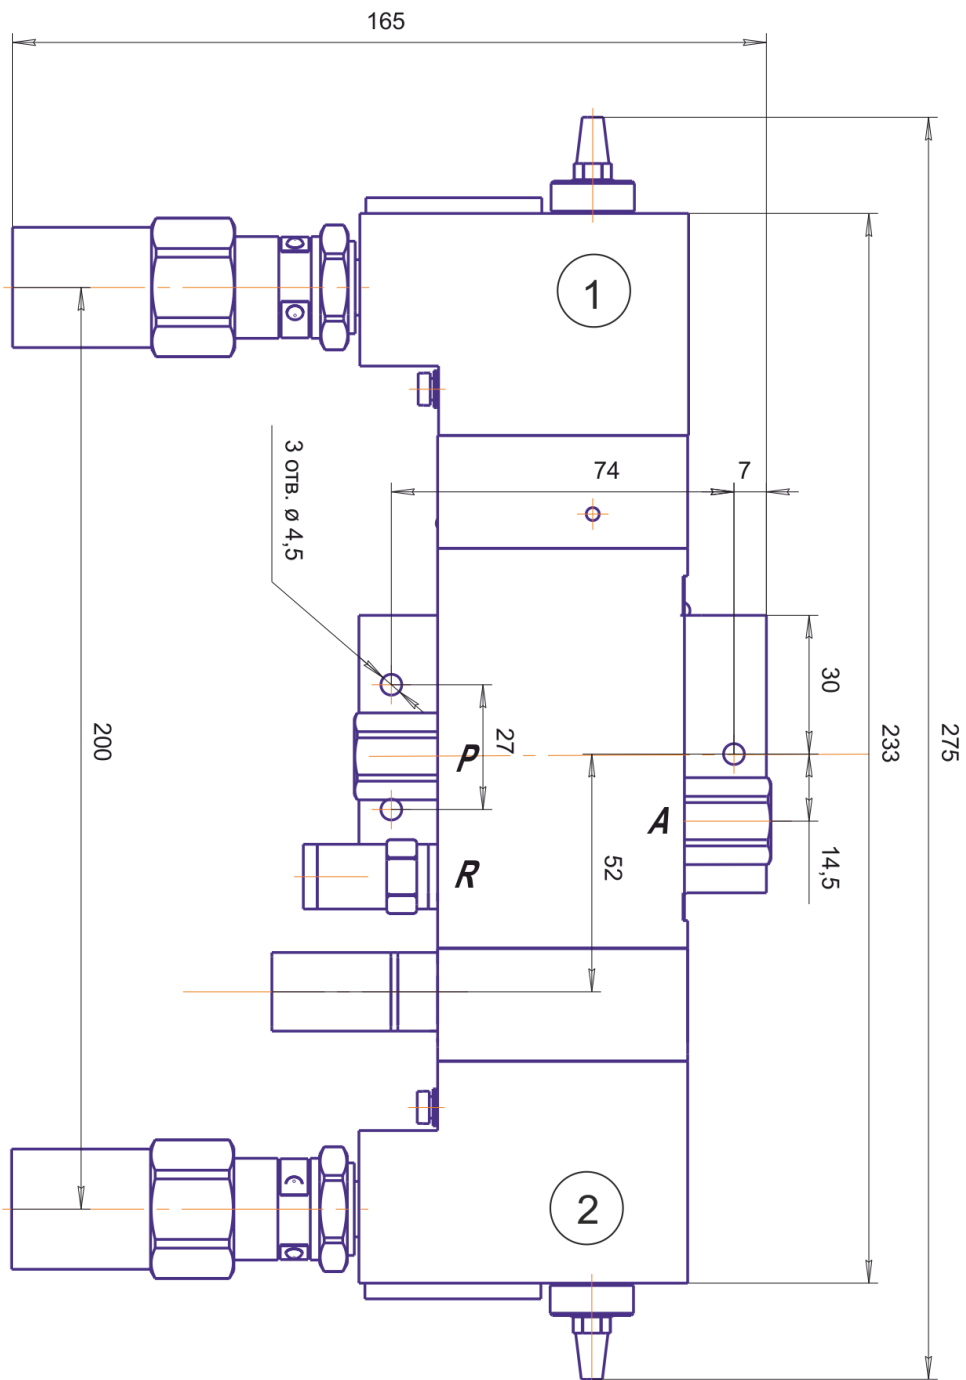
Габаритные и установочные размеры исполнений клапана КРВ-М-3/2-В- и КРВ-М-3/2-Д- с кабельным вводом для монтажа кабеля в металлорукаве РЗ-ЦХ-15
